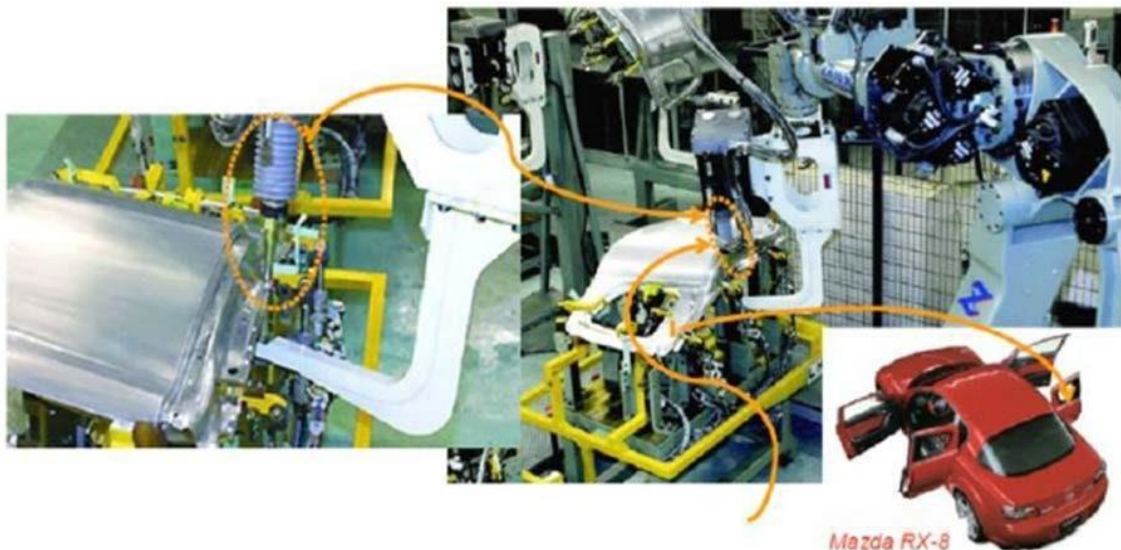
Soudage « friction-malaxage » par point utilisé pour l'automobile [31].
